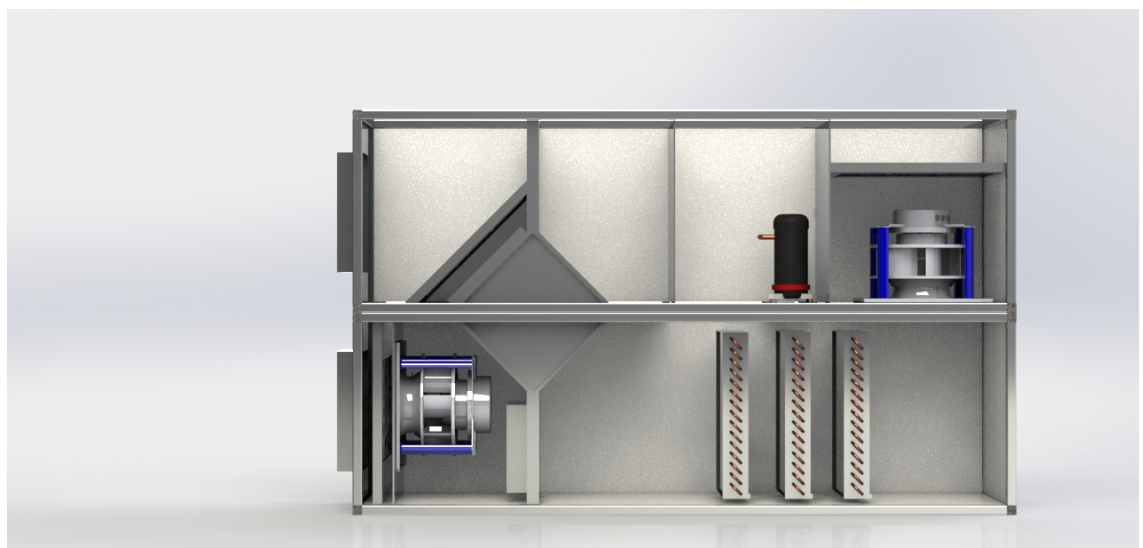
Diseño final de la máquina realizado con SolidWorks
